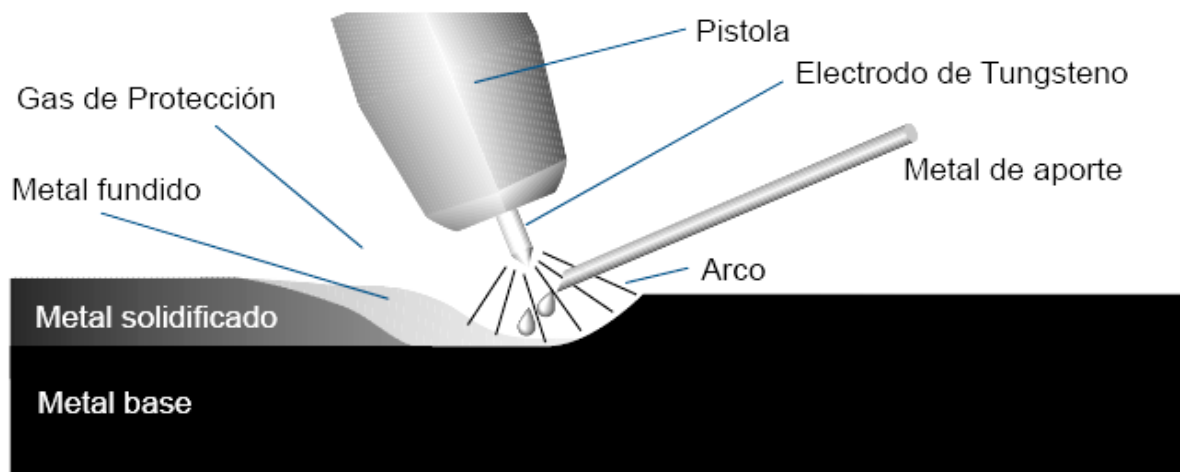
PROCESO DE SOLDADURA POR ARCO DE TUNGSTENO PROTEGIDO CON GAS.
